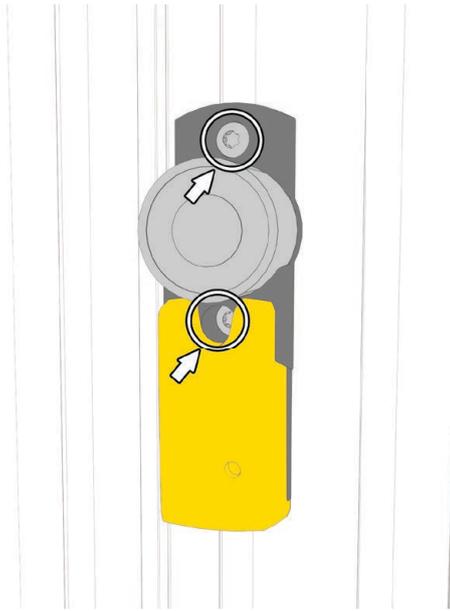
Prozesszuhalterung auf gewünschter Höhe am Profil anbringen und Schrauben M6 x 25 mm Torx festziehen.
